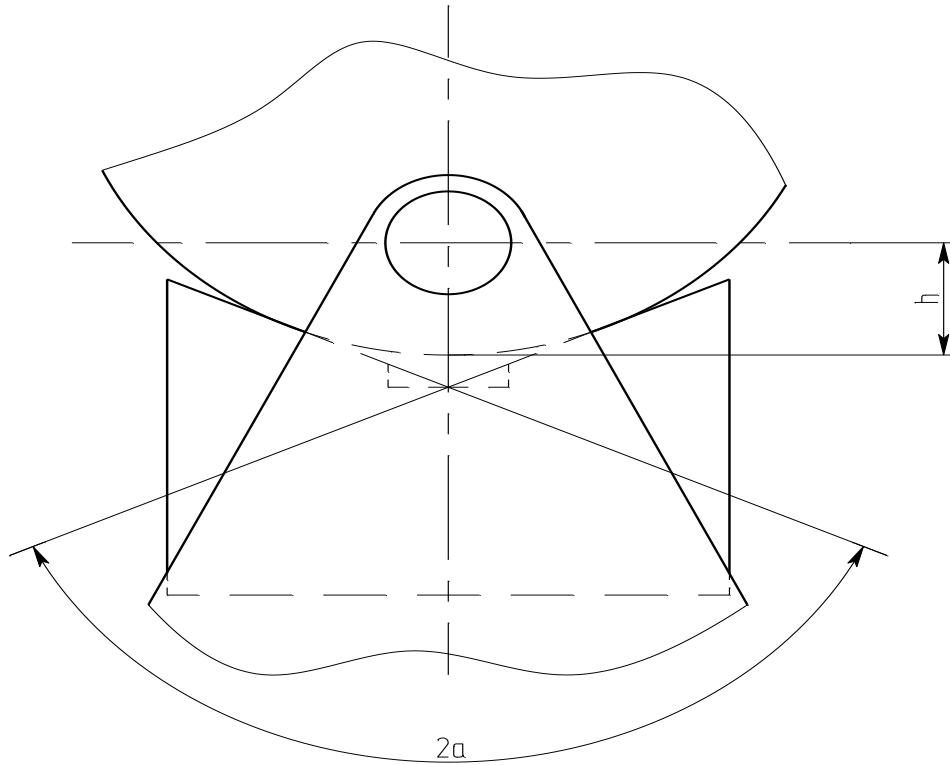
Схема базування деталі в призмі при свердлінні в кондукторі
